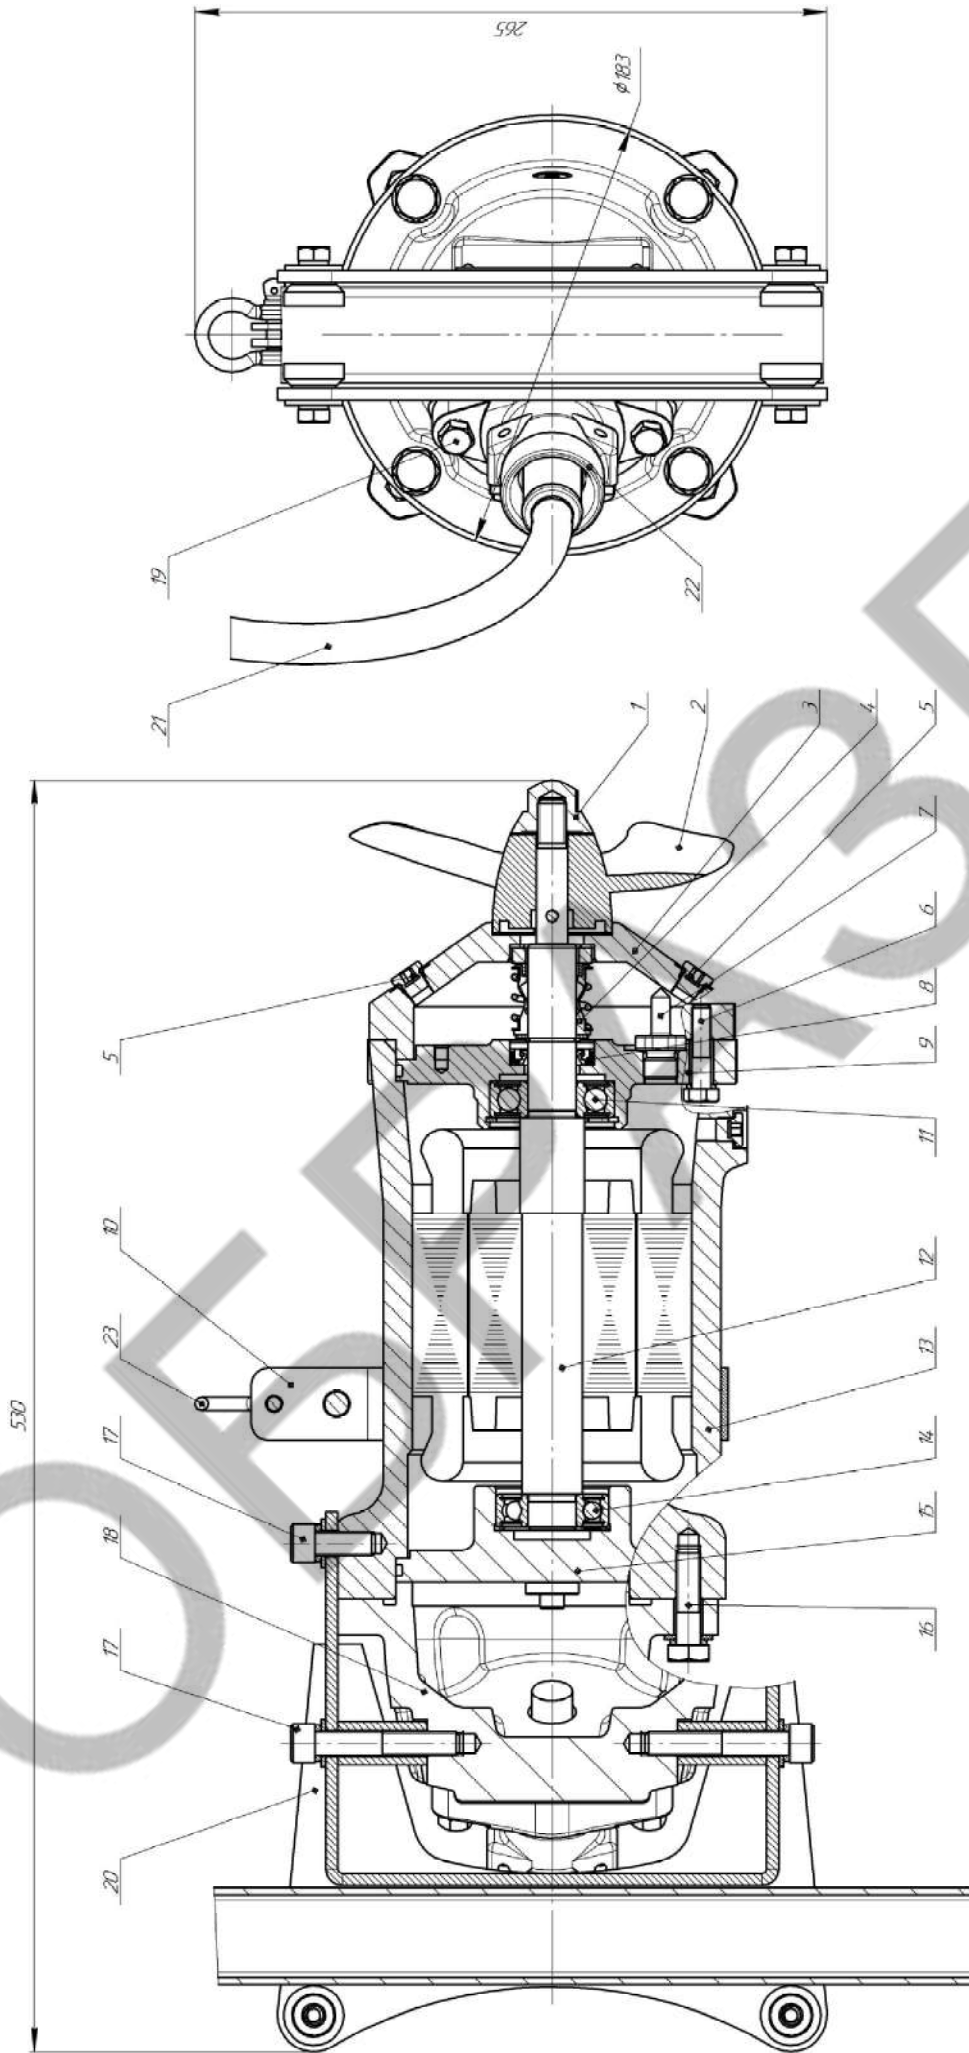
Общий вид и габаритные размеры мешалки "Иртыш" ПМ3 188 – 0,75/4
